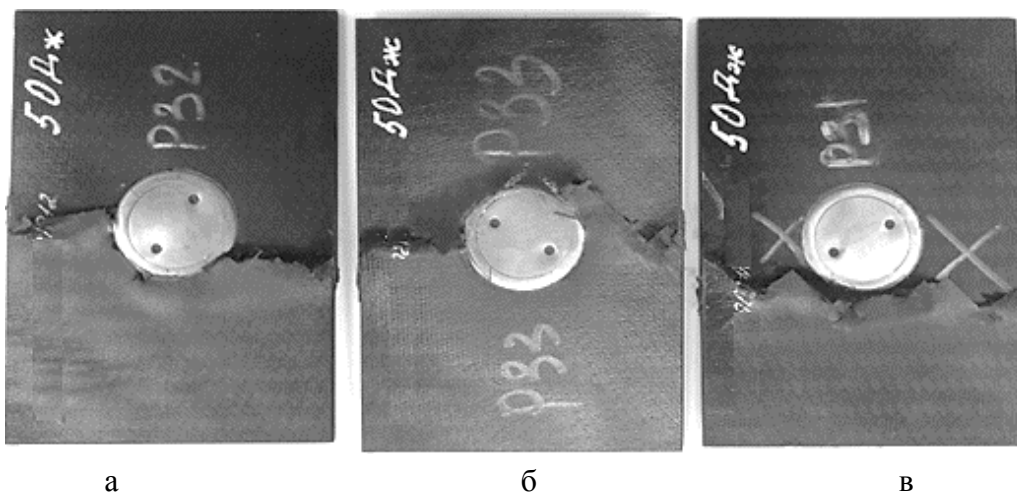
Фотографии образцов после сжатия. а) вставка установлена с натягом; б) вставка установлена с клеевой композицией, без натяга; в) вставка установлена с натягом и клеевой композицией.
